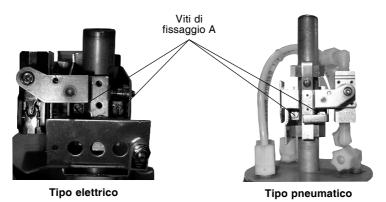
Meccanismo interruttore elettrico e pneumatico
